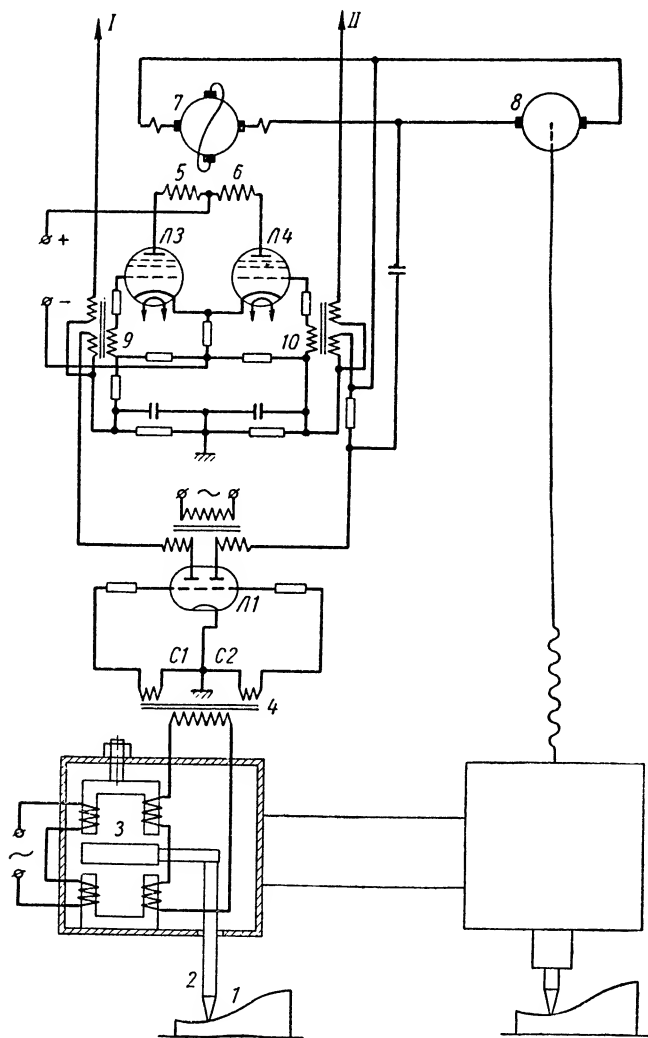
Схема движения изделия и фрезы в копирующе-фрезерном автомате:
